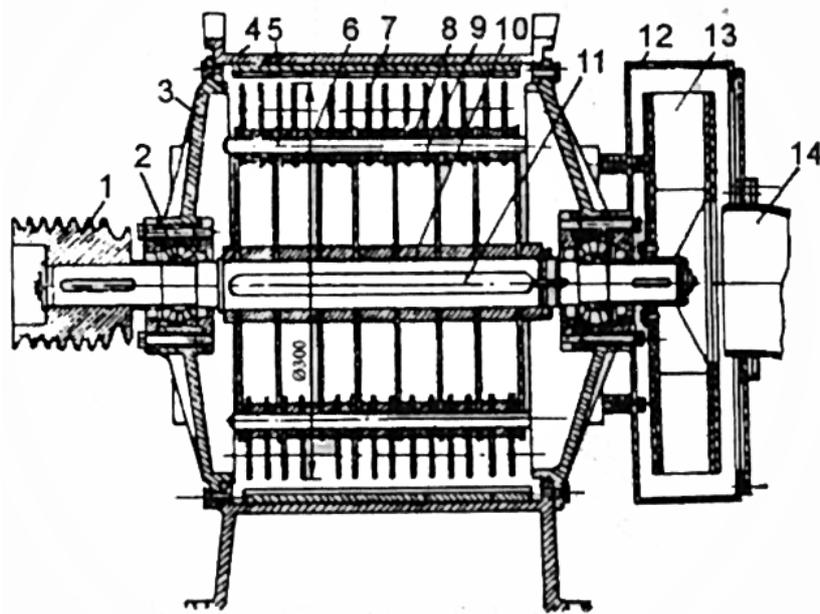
Молотковый барабан КДУ-2А с вентилятором:
